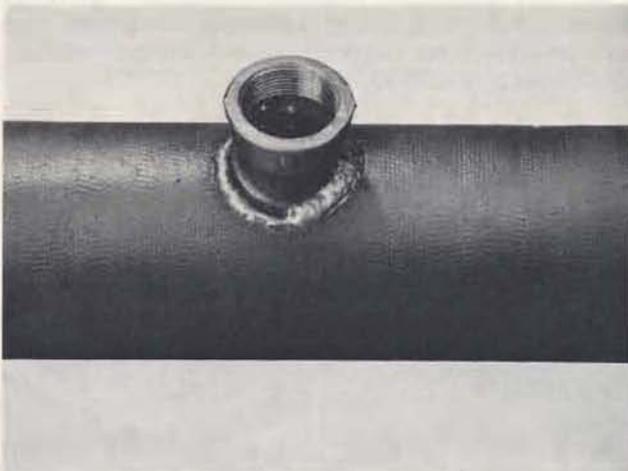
Stutzen beim Verschweißen mit Puffernaht
